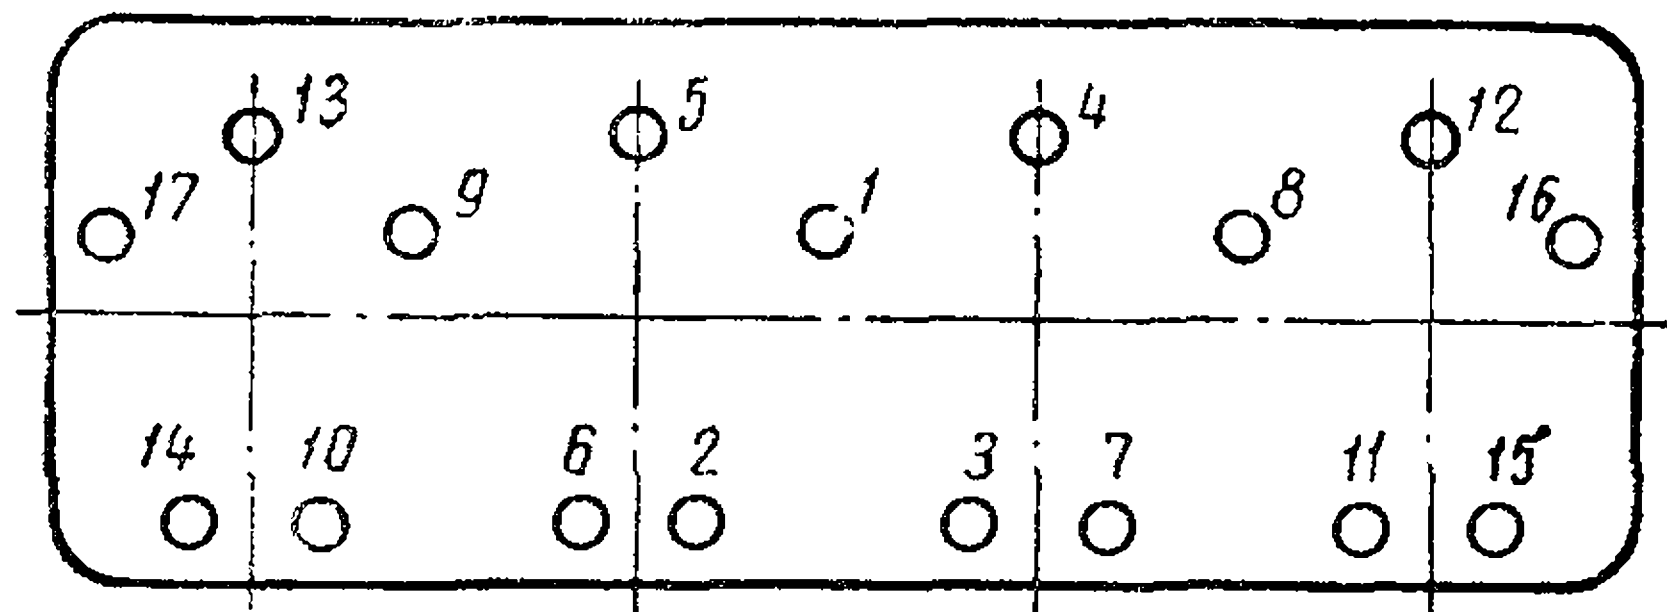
Порядок затягивания болтов крепления головки блока цилиндров
